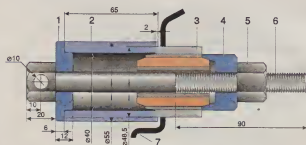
Замена резинометаллического шарнира нижнего рычага подвески: 1 – крышка; 2 – втулка; 3 – шарнир; 4 – оправка; 5 – гайка; 6 – болт; 7 – рычаг.
